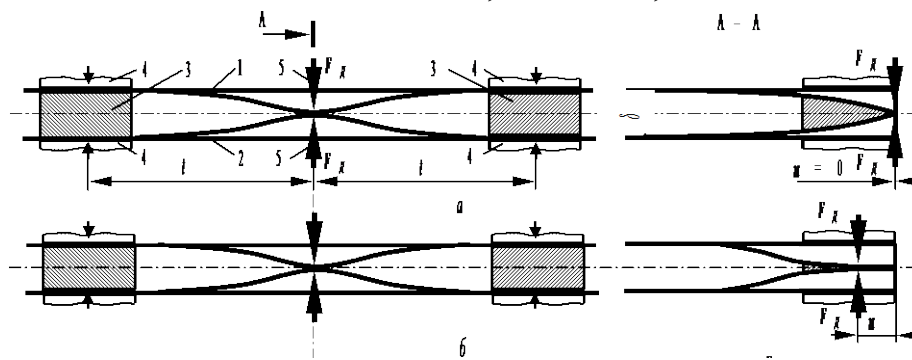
Схема деформації зварювальних деталей: 1, 2 – деталі; 3 – прокладка, що регулює величину зазору  $\delta$ ; 4 – стискаючі струбцини; 5 – електродний пристрій
